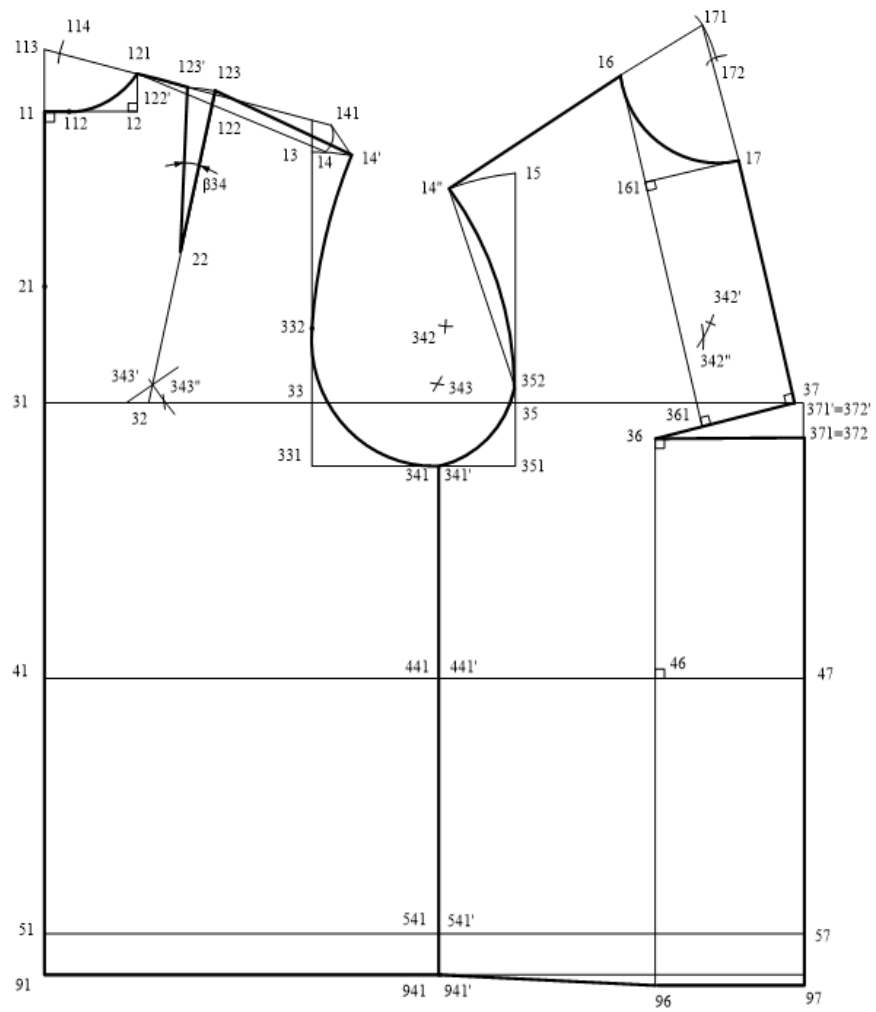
Базовая конструкция спинки и переда жакета
